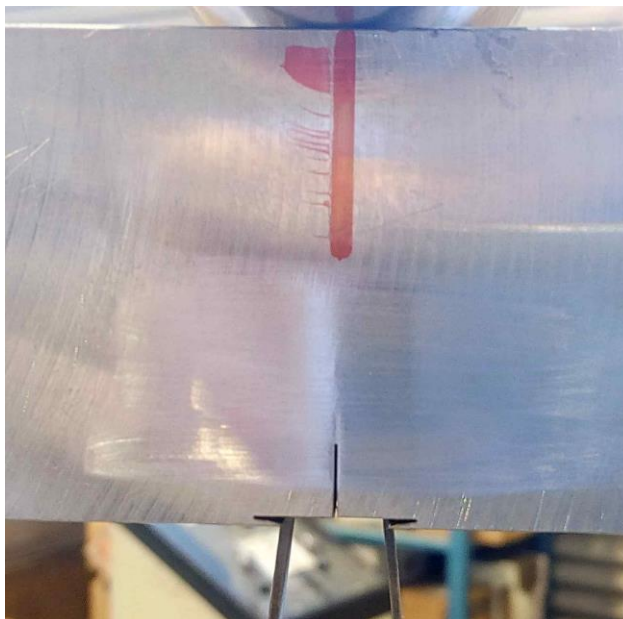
Entalla y grieta en probeta de fractura generada por EDM
